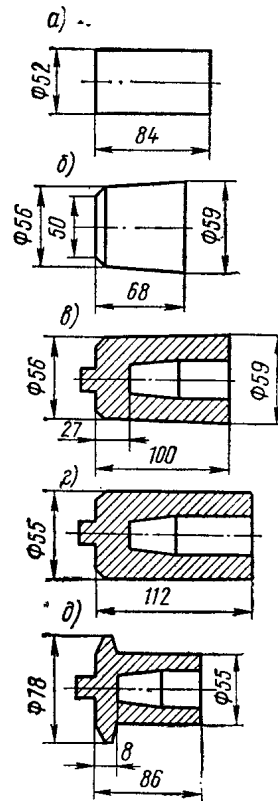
Схема последовательного применения закрытых (безоблойных) штампов при изготовлении пустотелых поволоков: а — мерная заготовка, б — осаживаемая заготовка, в — прошивка с обратным выдавливанием, г — калибровка стакана, д — высадка грибка
